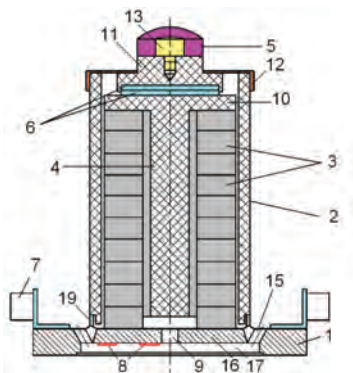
общий вид пьезоэлектрического вибратора, в частности фронтальный разрез
